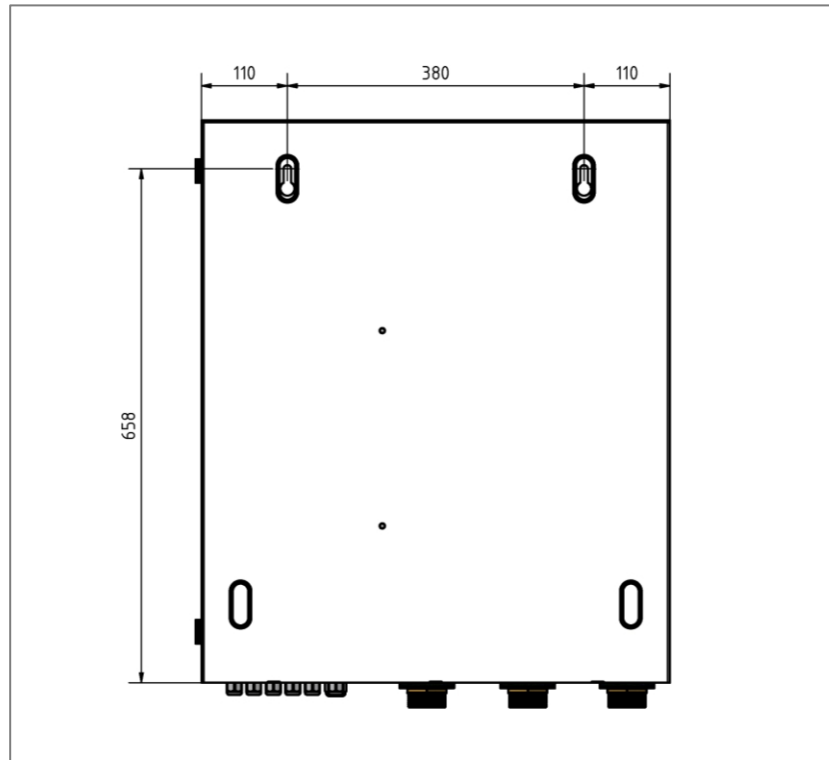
Paroi arrière du boîtier avec trous de montage, dimensions (mm)
